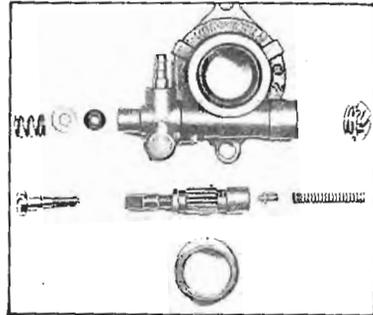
Despiece de una bomba automática de rotor accionada directamente desde el cigüeñal (DOLMAR).
